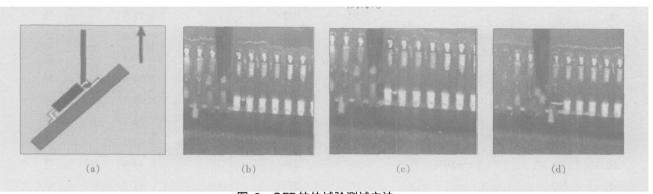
QFP拉伸试验测试方法 Fig. 2 Tensile test of quad flat pack
